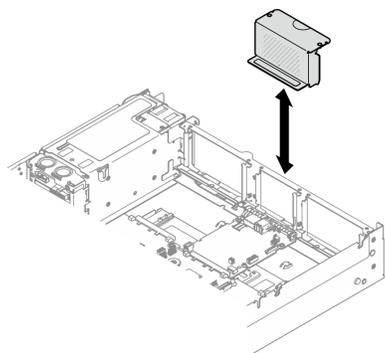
Installazione dell'elemento di riempimento della scheda verticale
